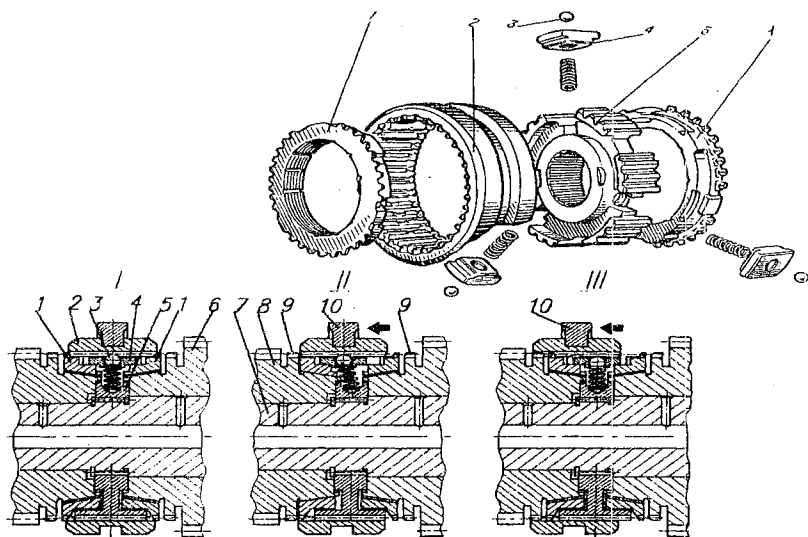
Детали и работа синхронизатора третьей и четвертой передачи автомобиля ВАЗ-2110:
